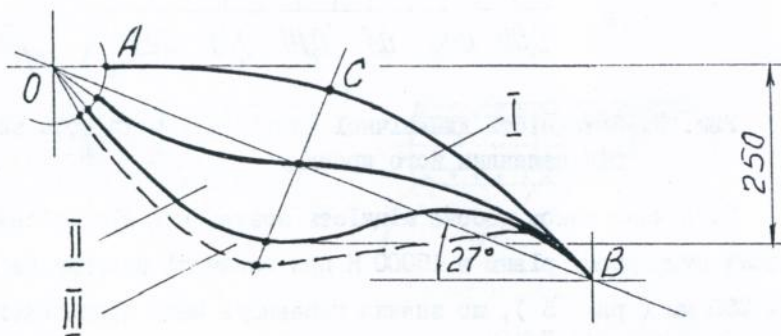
Ізолиї пересування точок робочої поверхні захисного зонта
